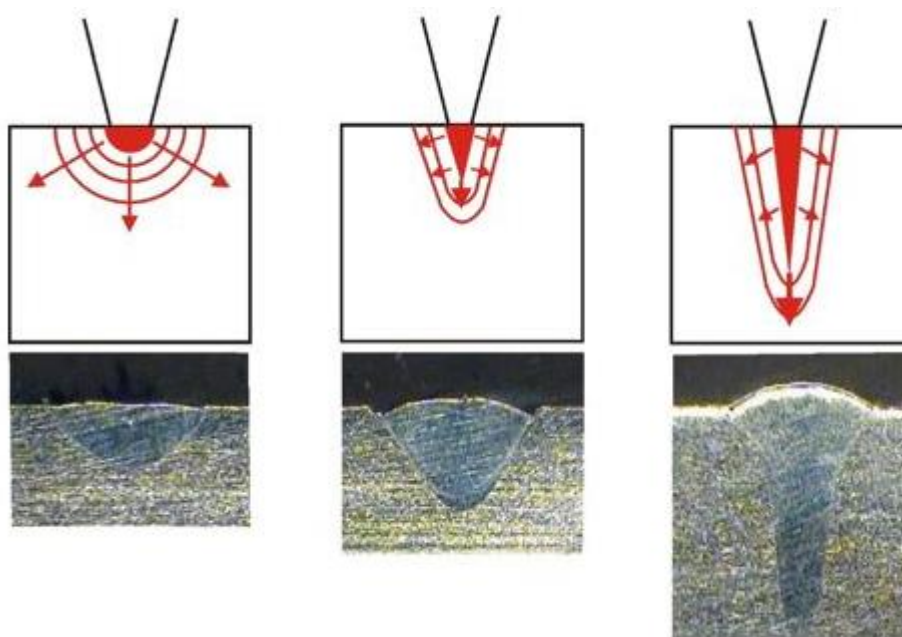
Transición de modo de soldadura láser por conducción a modo de soldadura por keyhole. [41]
